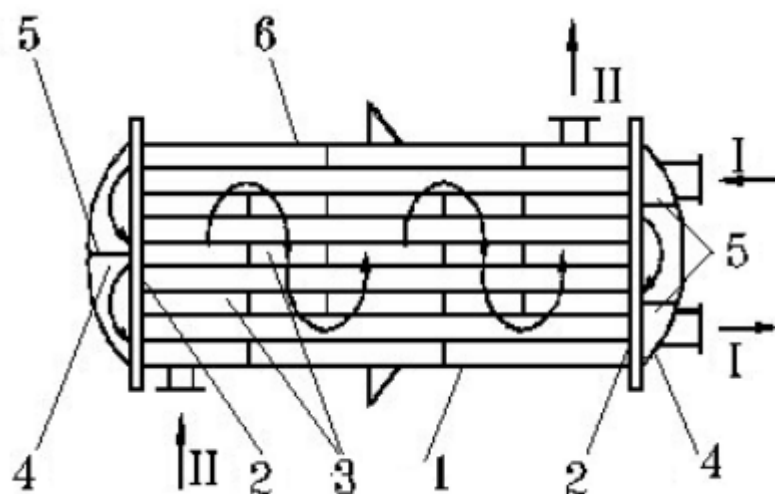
Кожухотрубчастий багатоходовий теплообмінники 1 - корпус; 2 – трубні решітки; 3 - труби; 4 - кришки; 5 - перегородки в кришках; 6 - перегородки в міжтрубному просторі.
